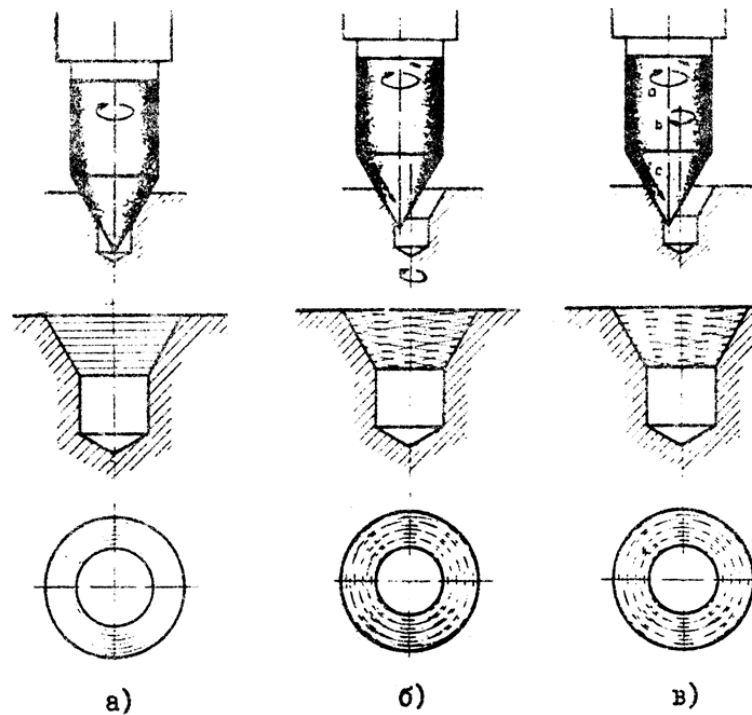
Схеми обробки центрових отворів на центр-шліфувальних верстатах
